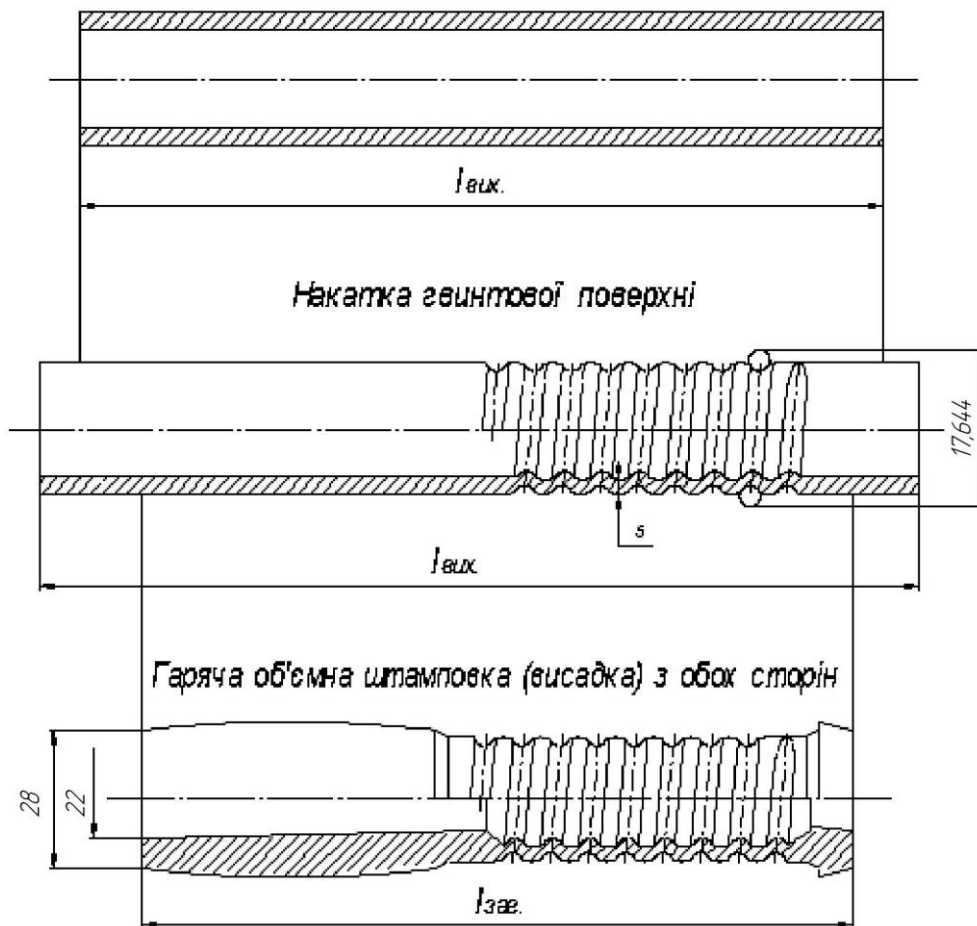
Переходи по виготовленню заготовки гвинта
